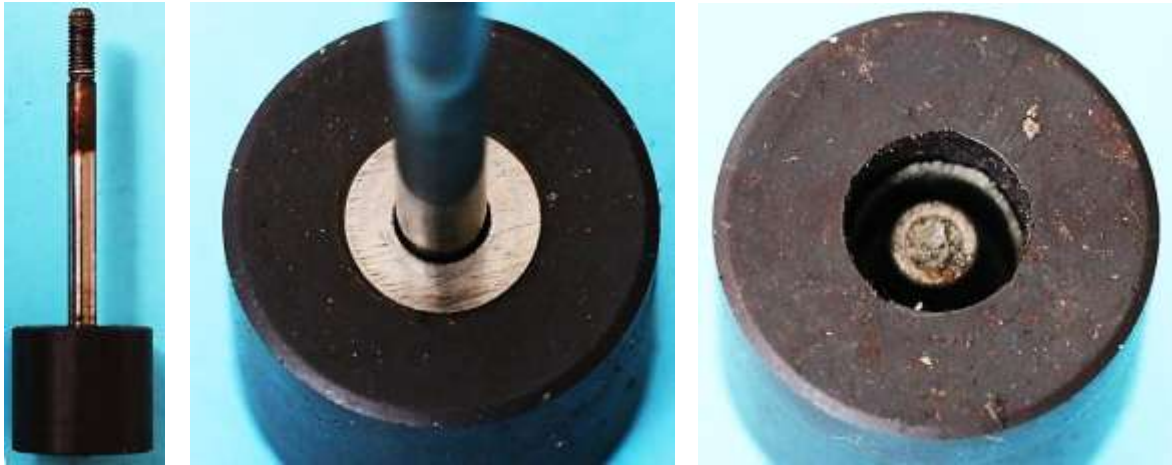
Polrad: Durchmesser 24 mm, Länge 21 mm
